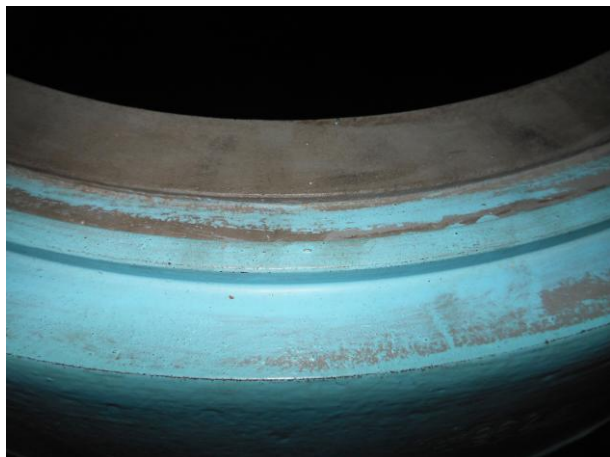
Осмотр уплотнительной поверхности втулки, сопрягаемой с крышкой цилиндра дизеля типа 8ZD72/48
